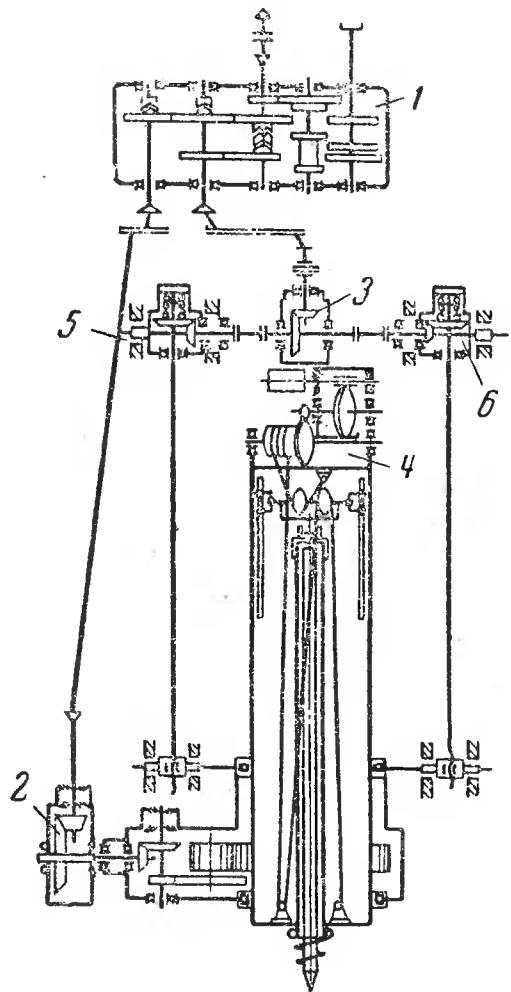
Кинематическая схема привода рабочего органа машины МЗС-13.
